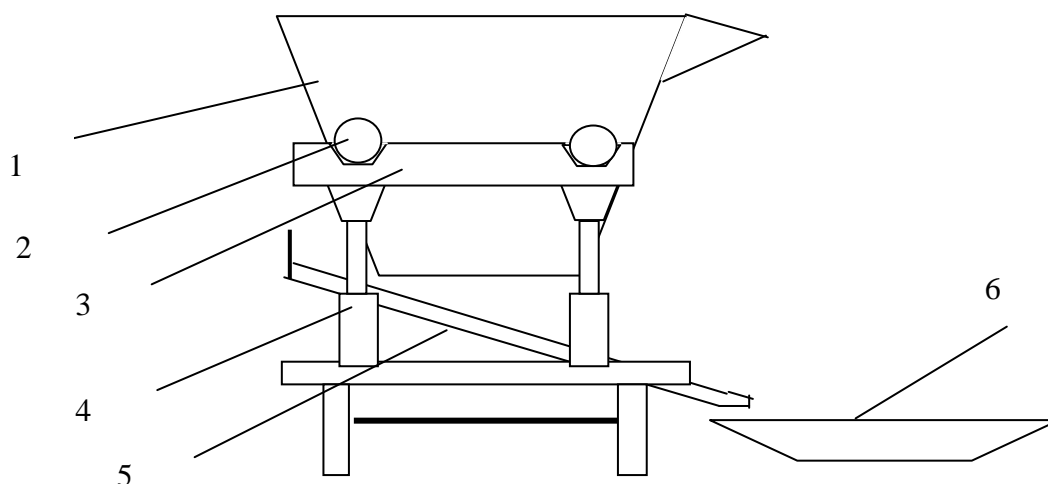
Схема установки промежуточного ковша на тележке
